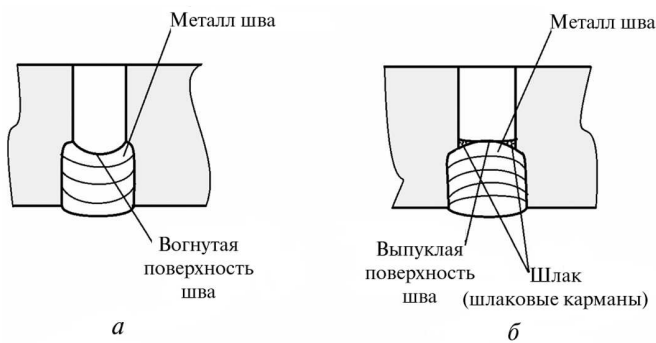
Расположение шлаковых карманов в сварном шве:
